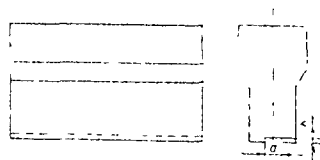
Доработка поддержек 54389-11 групповых штампов для клепки заклепок с плоско-выпуклыми головками
